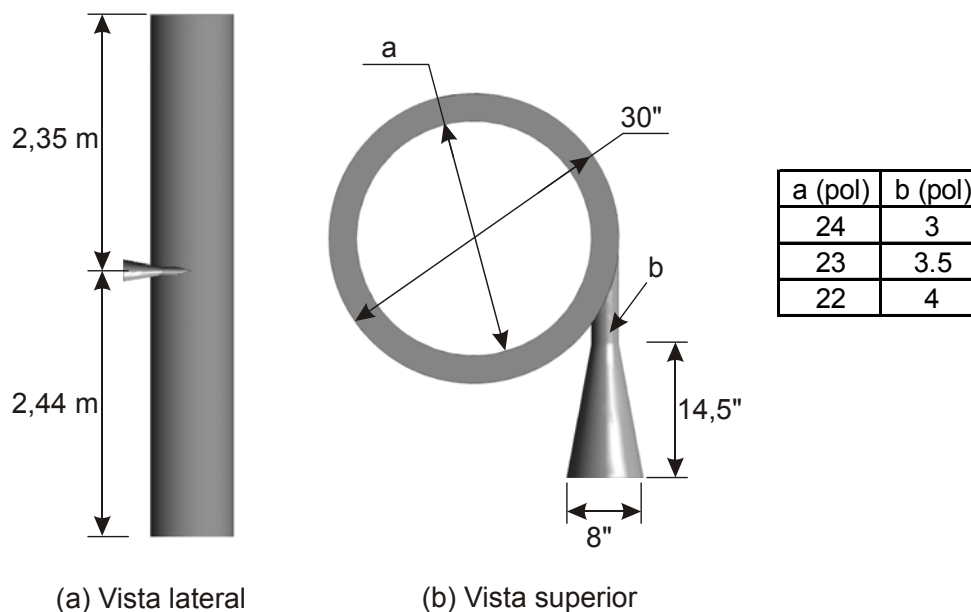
Desenho com as dimensões da câmara de expansão.
